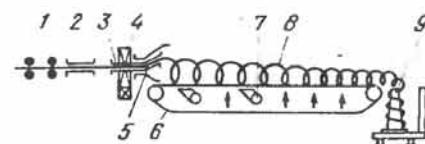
Схема устройства двухстадийного охлаждения катанки:
